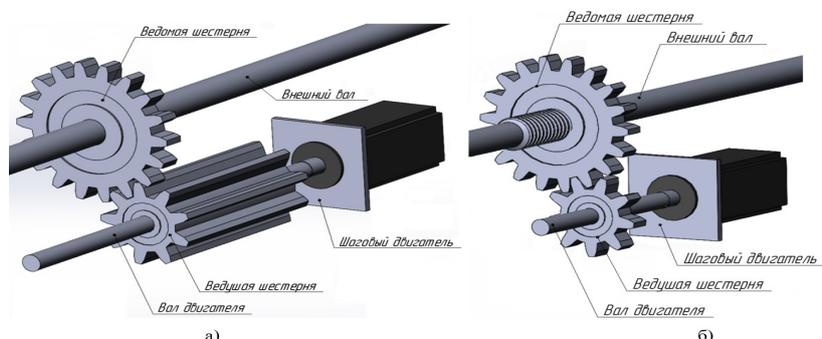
3D-вид механизмов для передачи движения КА закрепленному в фиксирующей рамке: а) вращательного, б) возвратно-поступательного.
